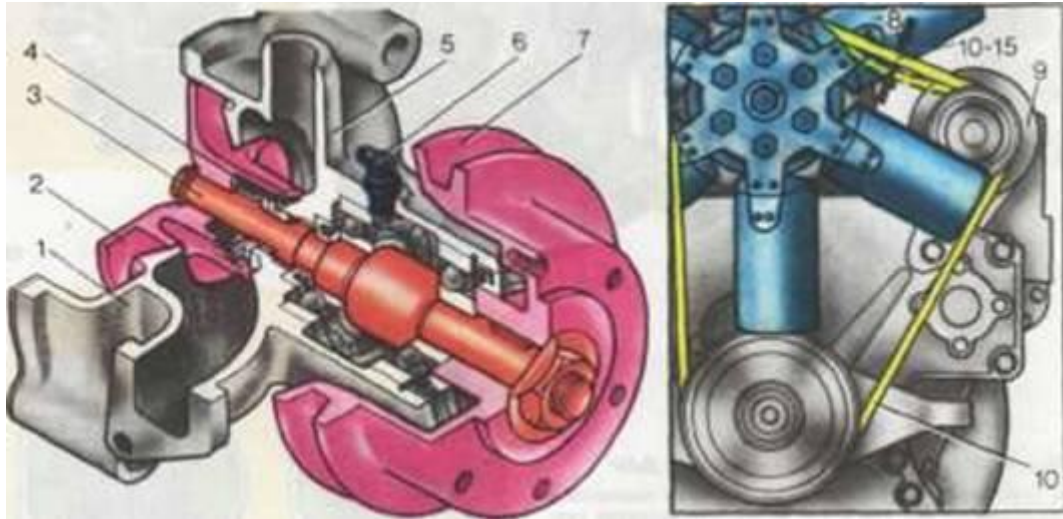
Водяний насос двигуна Д-240: А -будова, Б - привод. 1 - корпус, 2 - крильчатка, 3 -валик, 4 – ущільнювальний пристрій, 5 - верхній патрубок, 6 - масльонка, 7 - шків, 8 - хрестовина вентиляторів, 9 - генератор, 10-пас.
